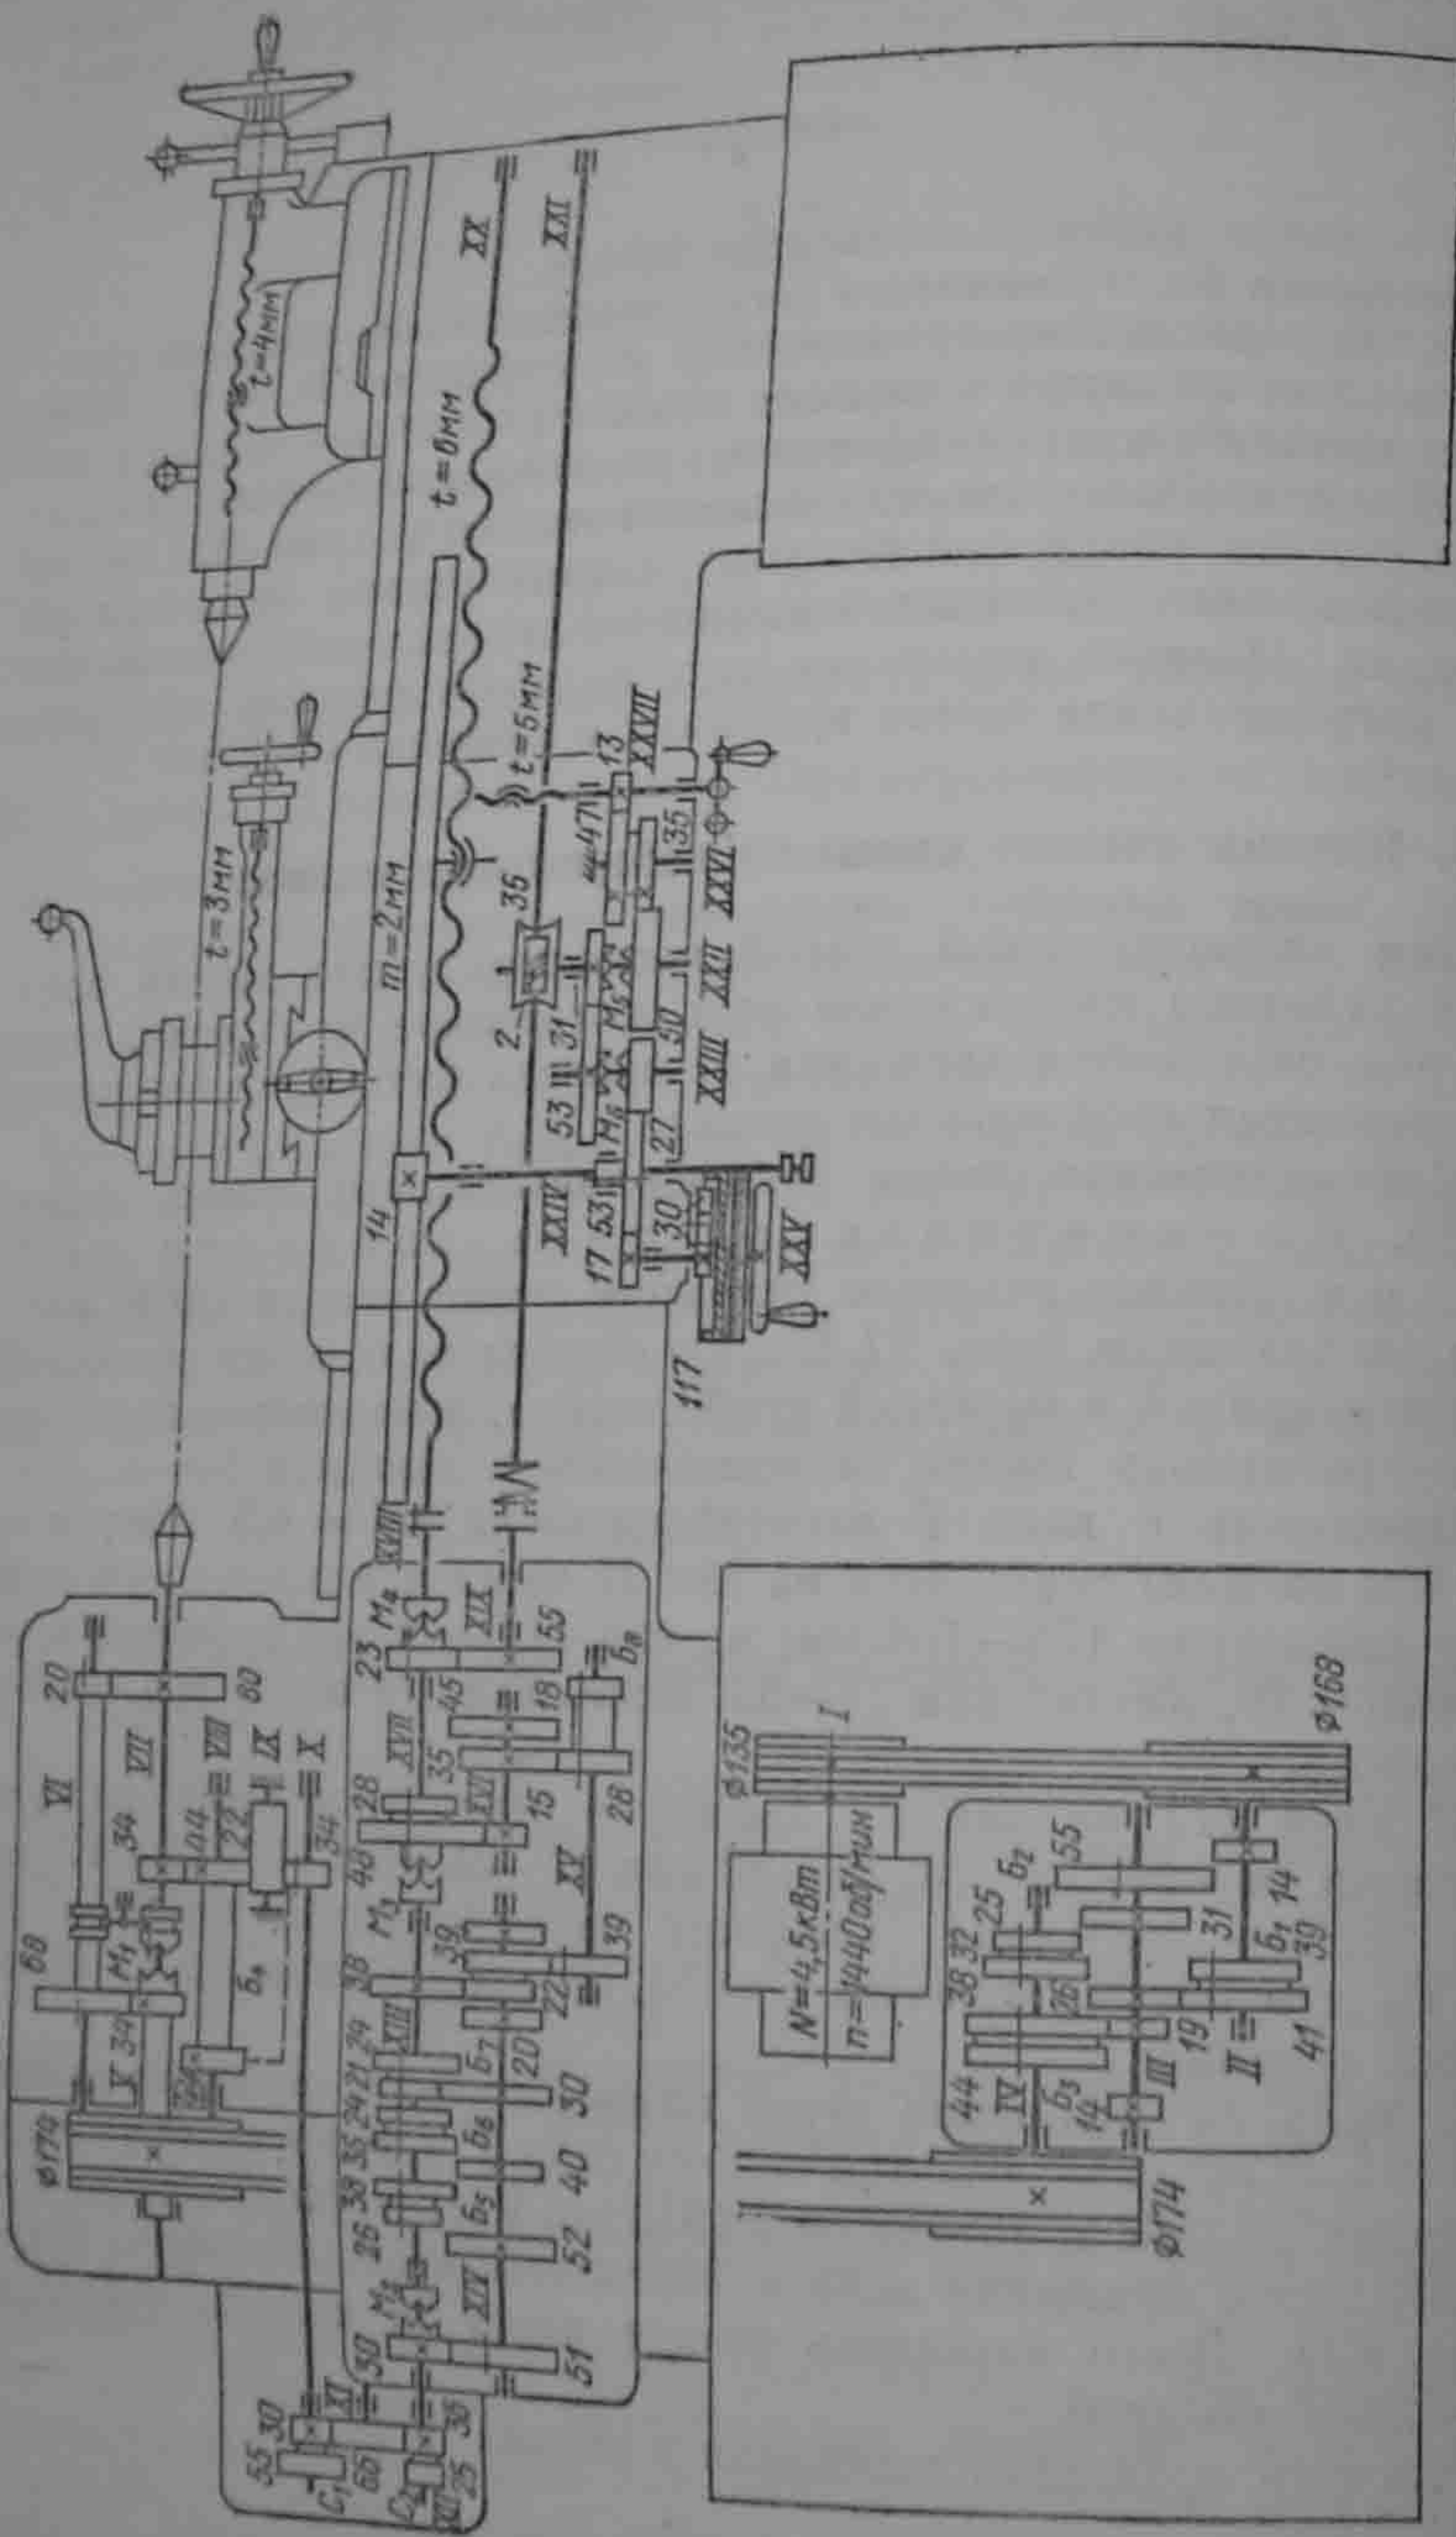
Кинематическая схема токарно-винторезного станка модели 1А616
